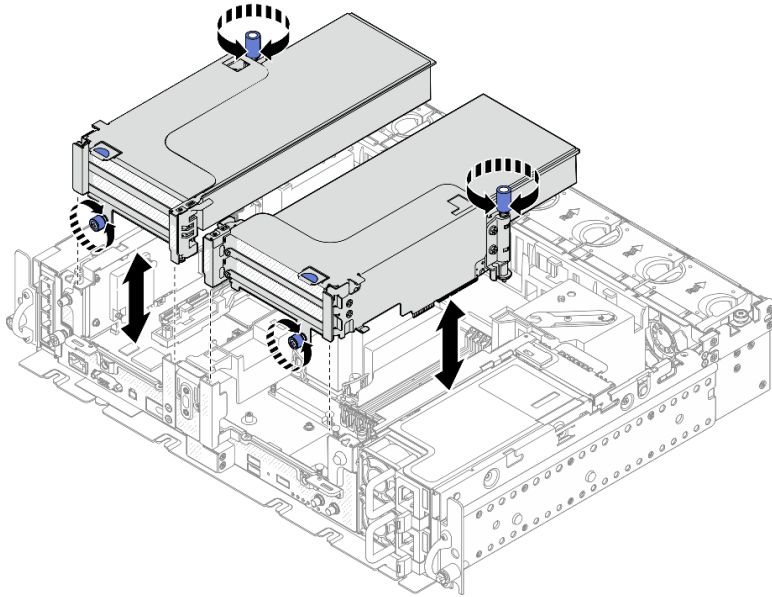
Entfernen der PCIe-Adapterkartenbaugruppen mit Adaptern mit voller Langer
